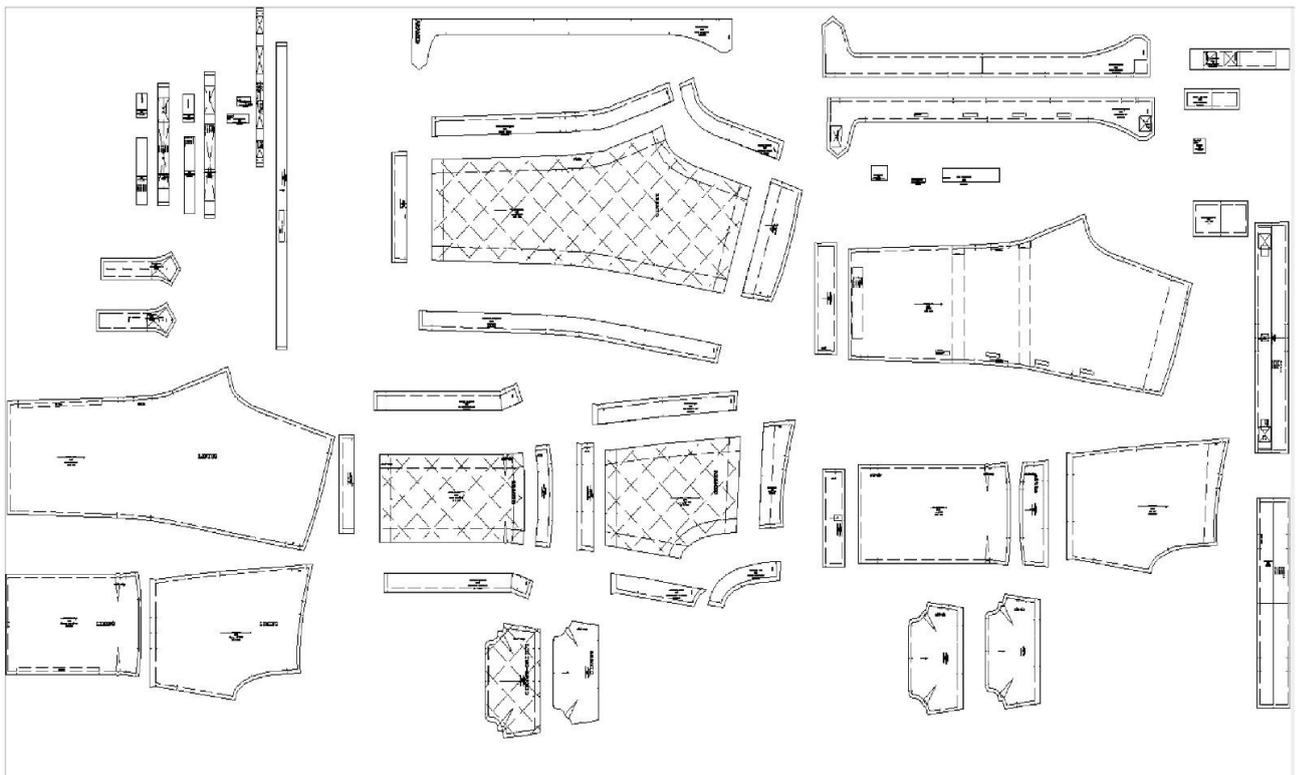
Орієнтовний зовнішній вигляд деталей елемента 2
